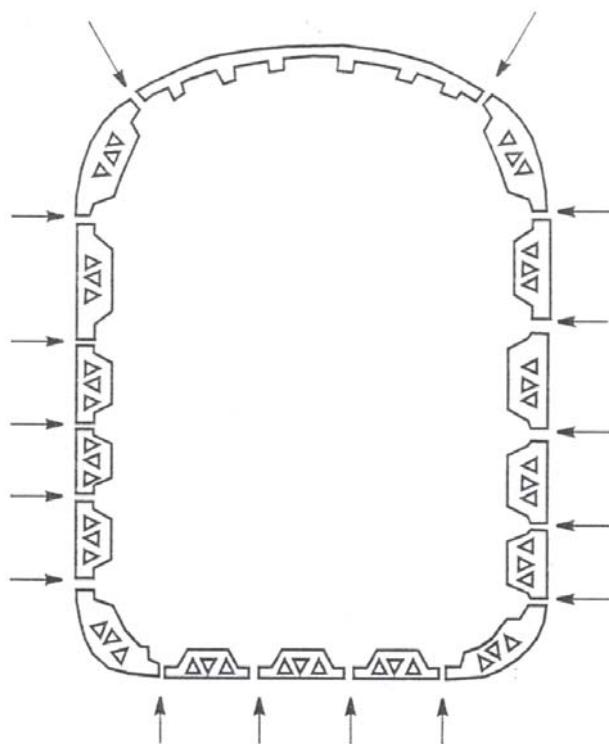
Конструктивно-технологическая разбивка кузова вагона из полых панелей (стрелками отмечены места расположения продольных сварных швов)
